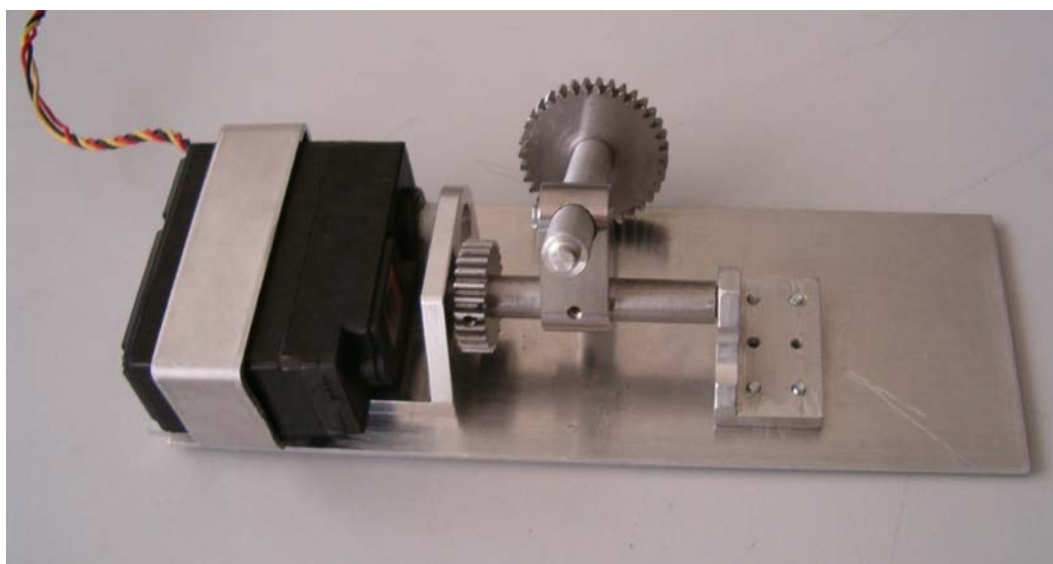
Garantir o entre-eixo entre o motor e a roda.
